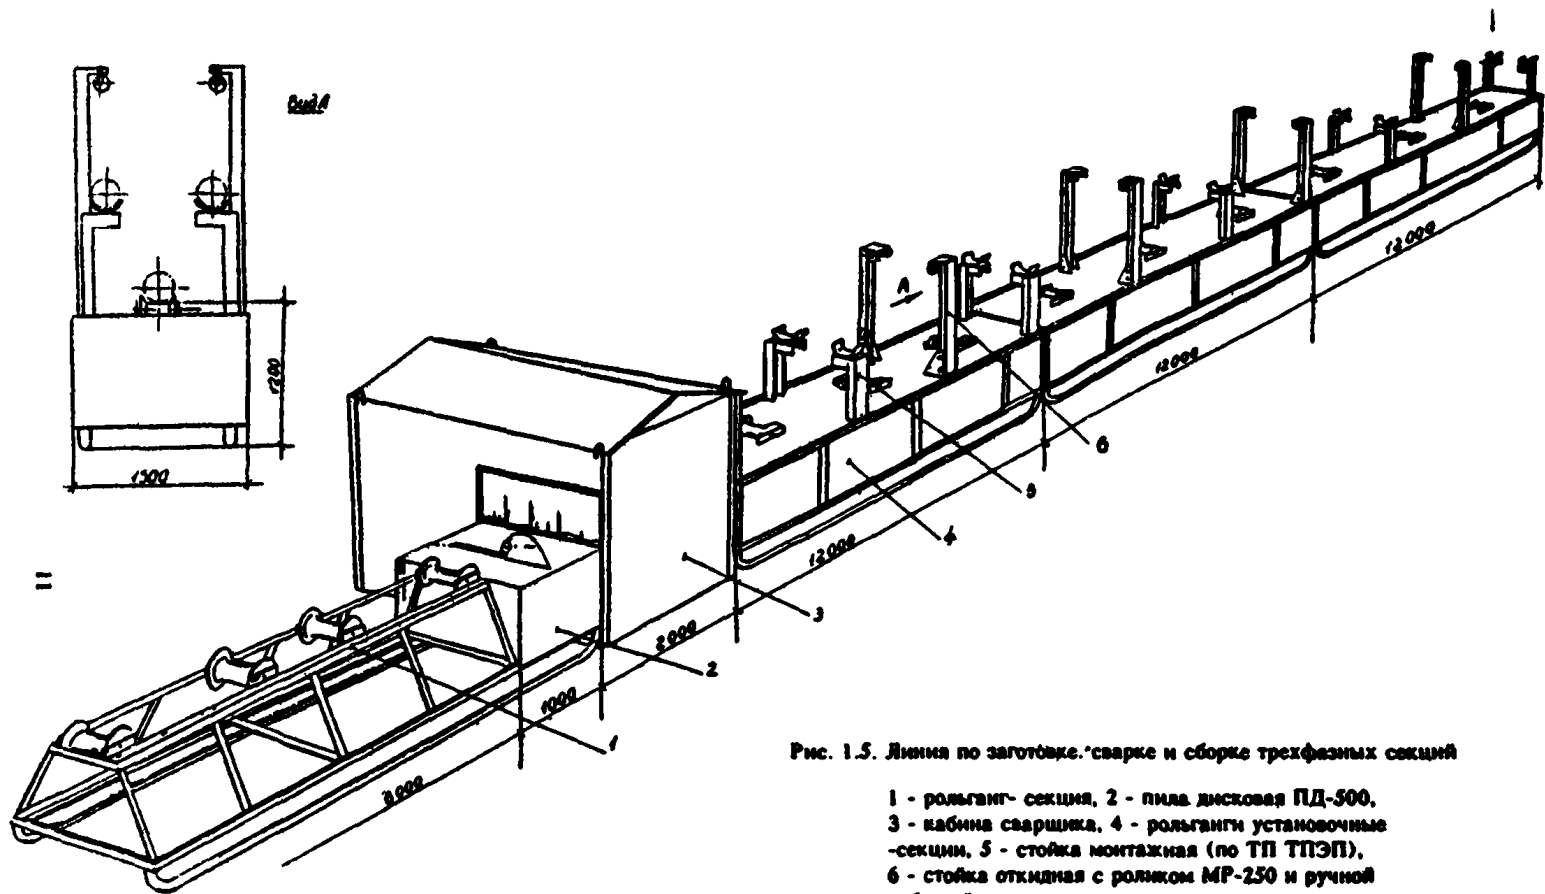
Линия по заготовке, сварке и сборке трехфазных секций
